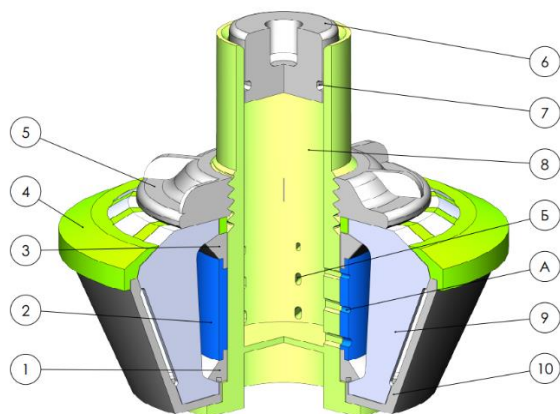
Конструкція пресформи для виготовлення ущільнювача превентора 1 – вкладиш нижній; 2 – втулка; 3 – вкладиш верхній; 4 – кришка; 5 – гайка; 6 – поршень; 7 – ущільнення поршня; 8 – циліндр; 9 – вставка; 10 – корпус
